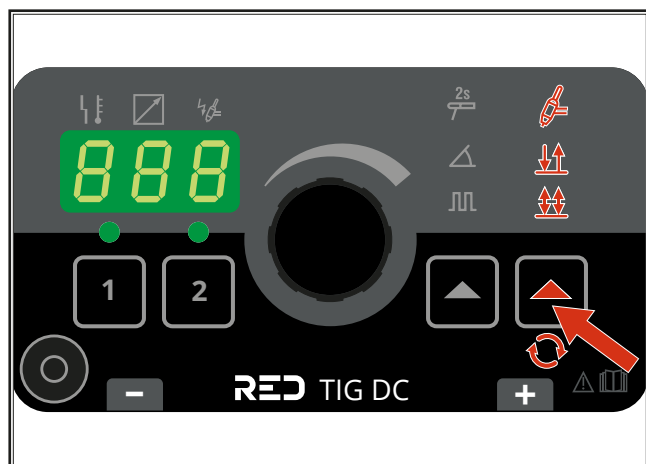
Ajustar el proceso de soldadura y el modo de funcionamiento
